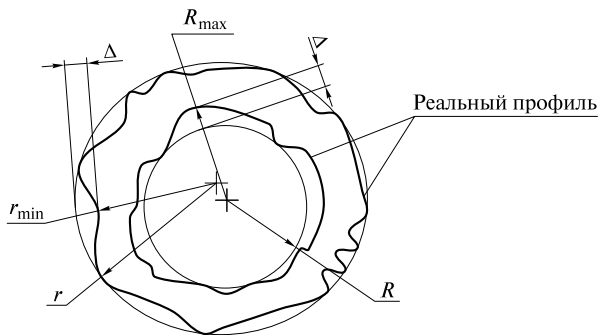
Схема расположения прилегающего цилиндра для наружной и внутренней поверхностей:
